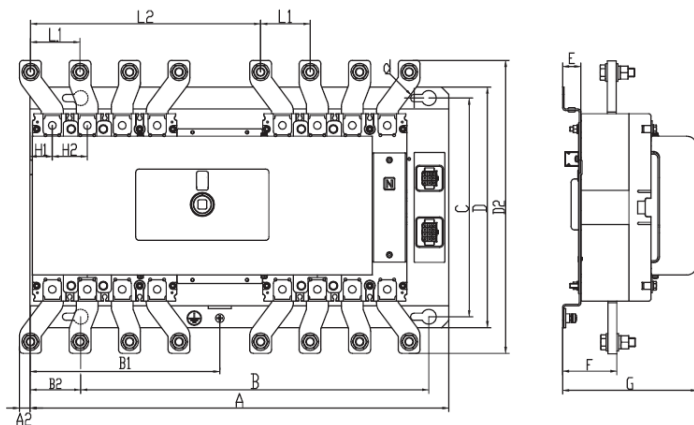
Габаритные размеры АВР-300 400-630А/3Р, 4Р в разъемном корпусе
